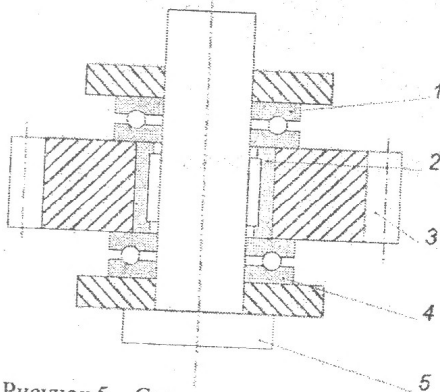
Схема приспособления для обкатки зубчатых колес
